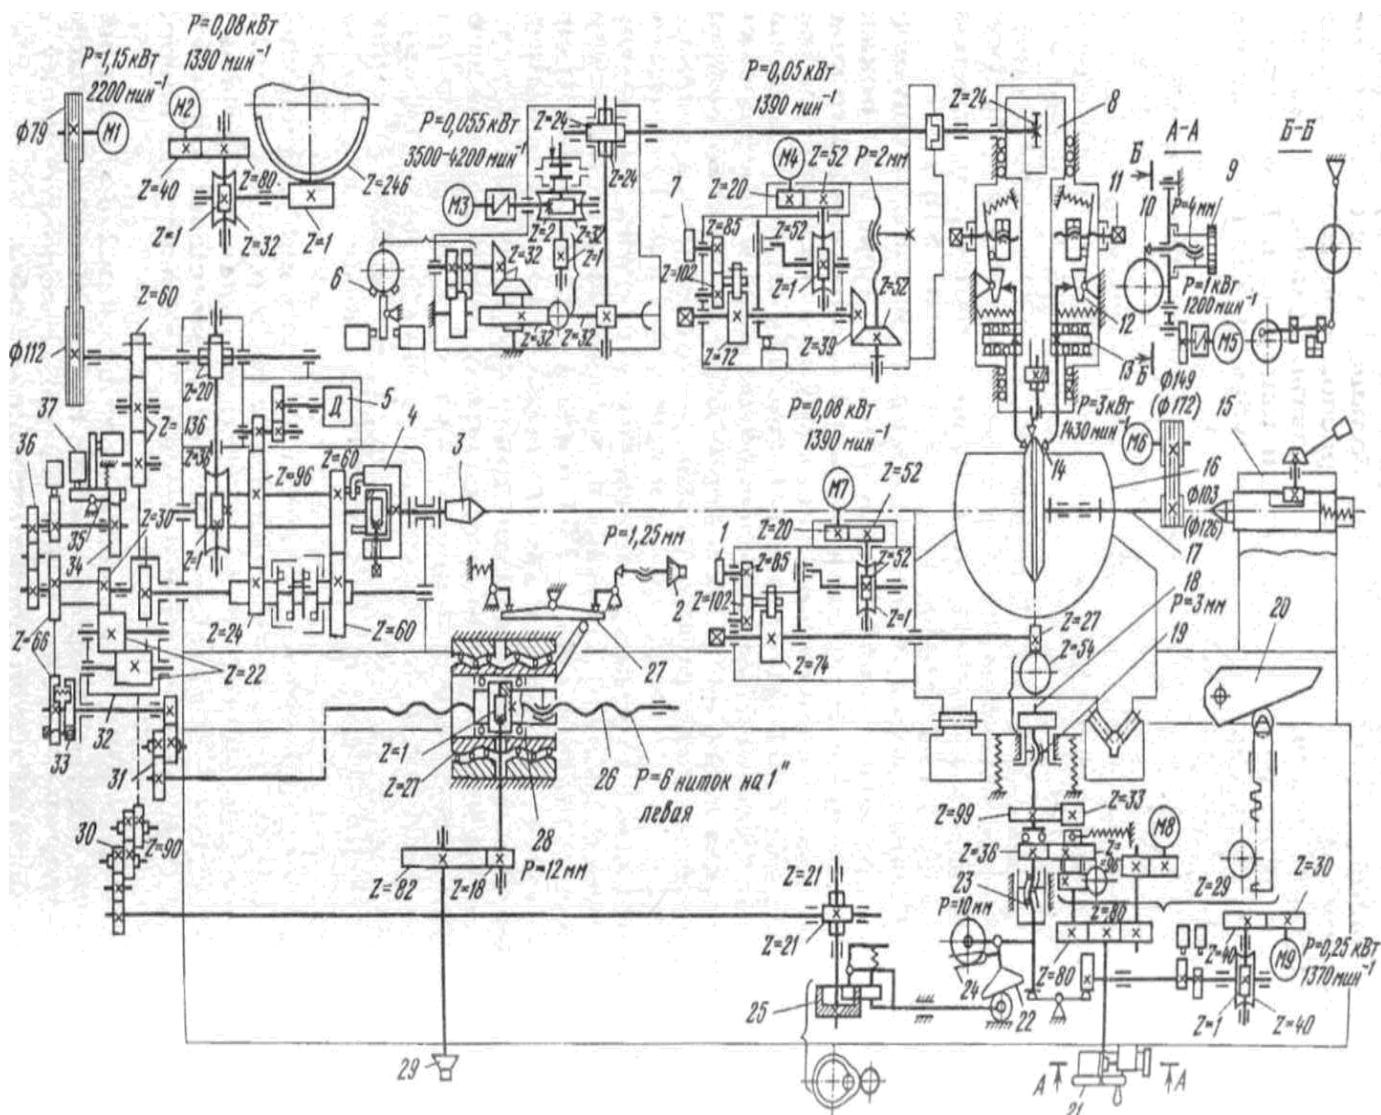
Кинематическая схема универсального резьбошлифовального станка без ЧПУ.
